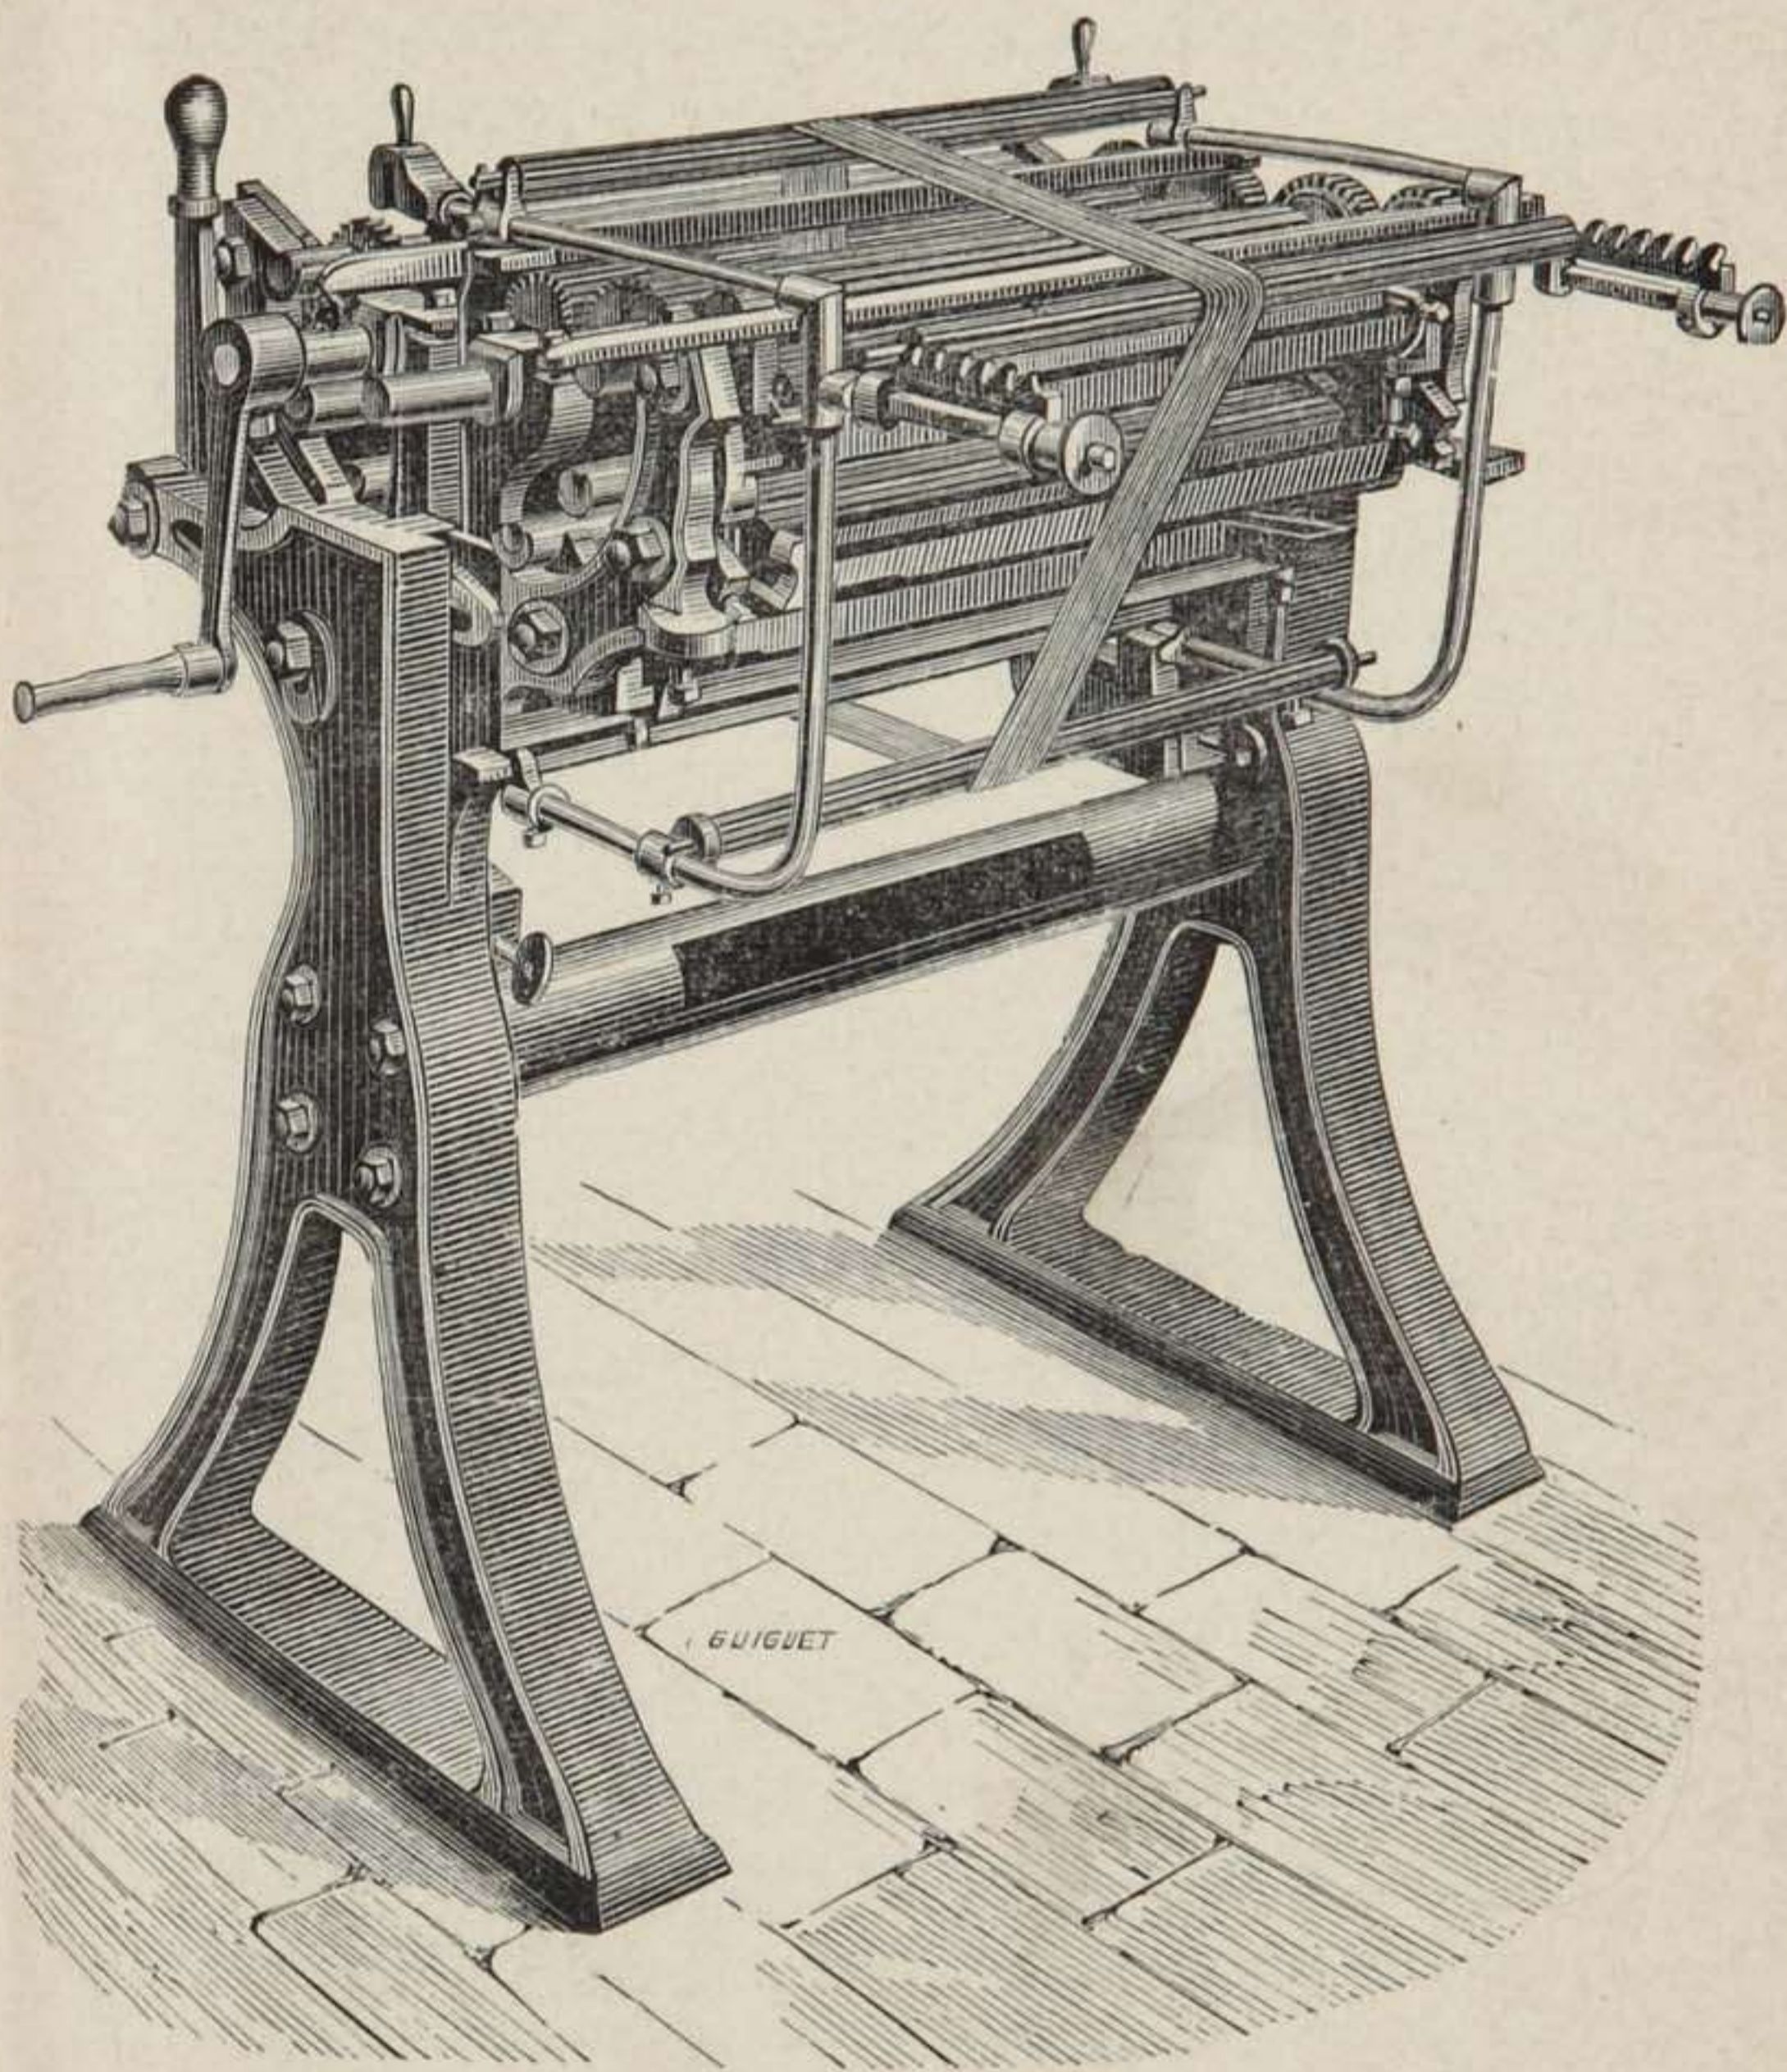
Machine à imprimer les écheveaux à six couleurs.
